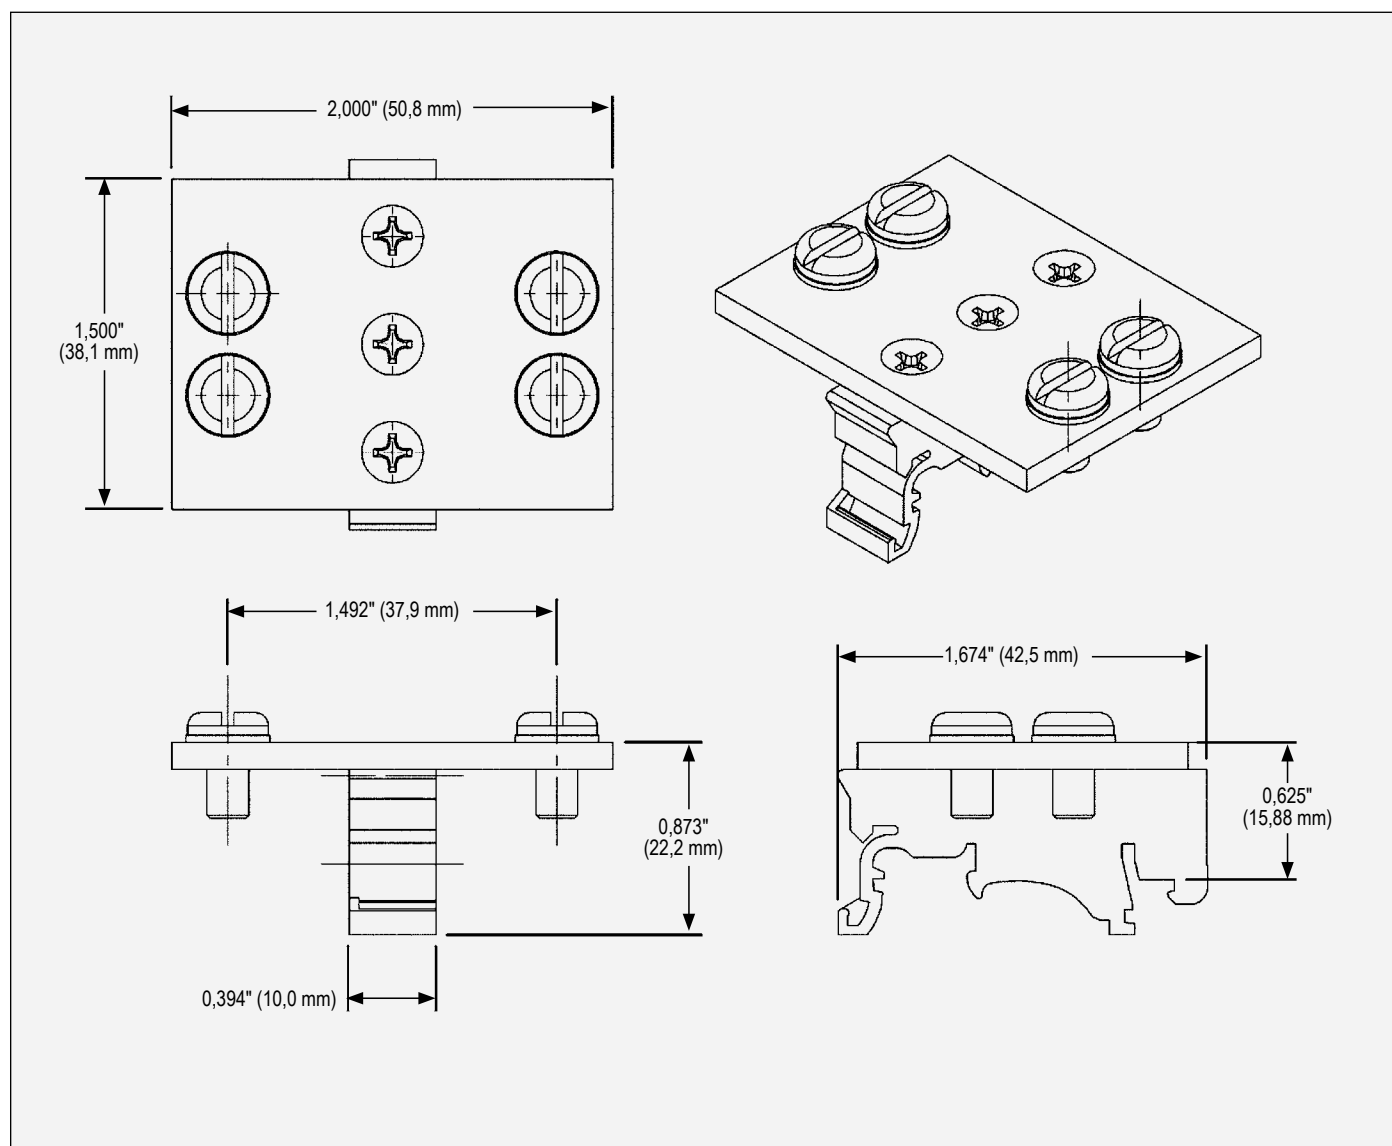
Dimensioni kit di montaggio guida DIN solenoide
